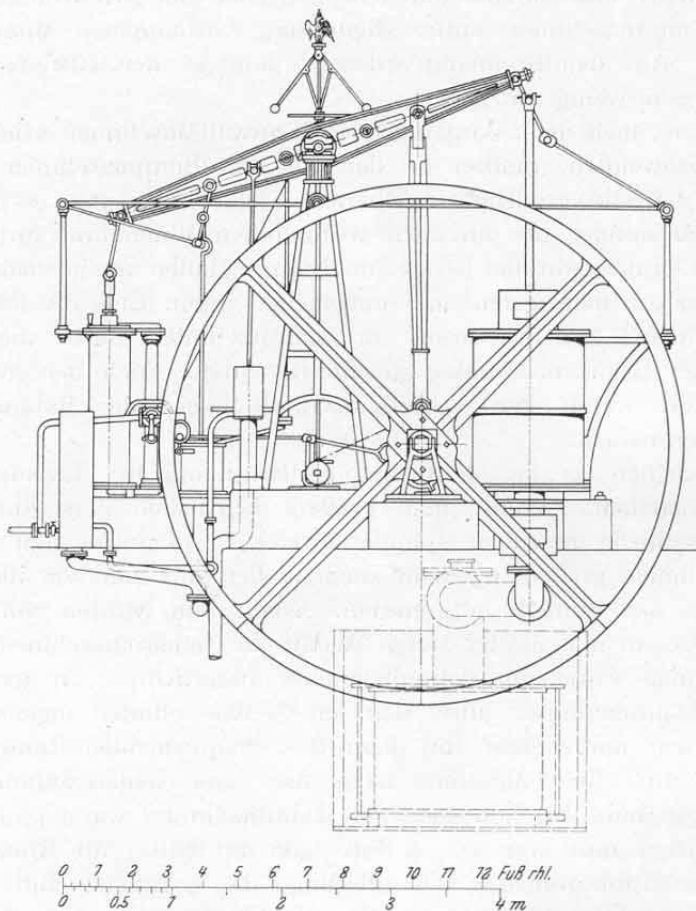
Gebläsemaschine mit Drehbewegung von Freund-Berlin 1820.
